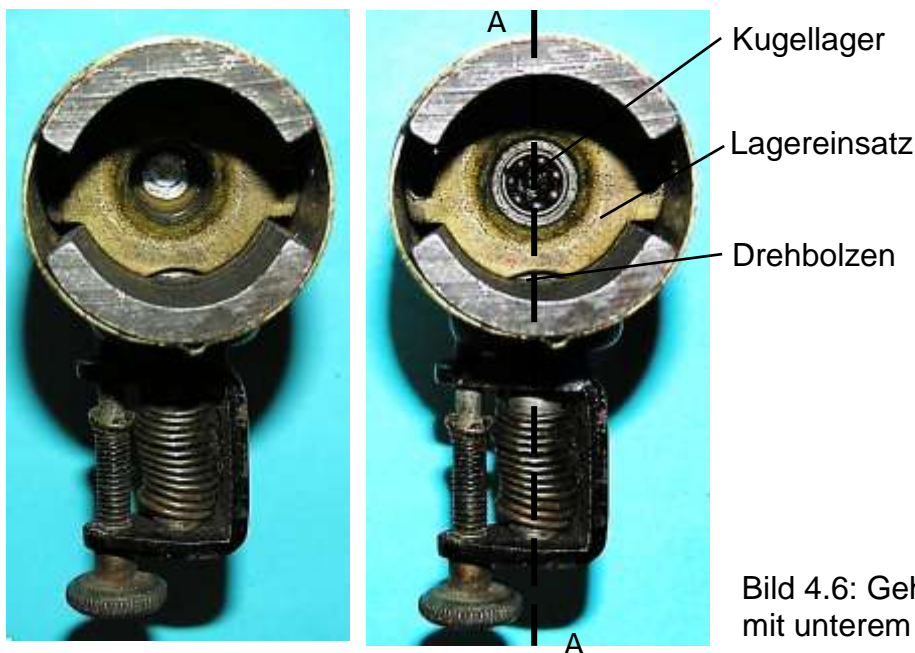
Gehäusetopf ohne und mit unterem Kugellager
